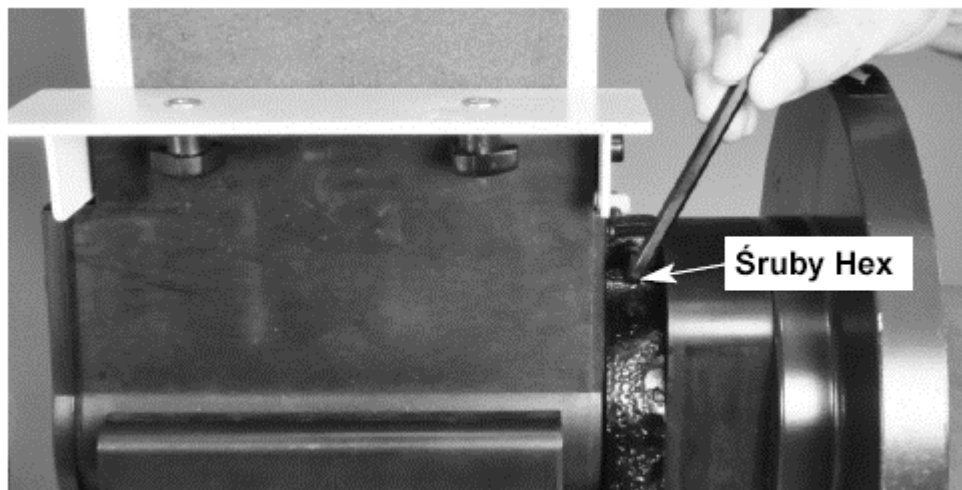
ODLEGŁOŚĆ STOLIKA OD POWIERZCHNI SZLIFUJĄCEJ
